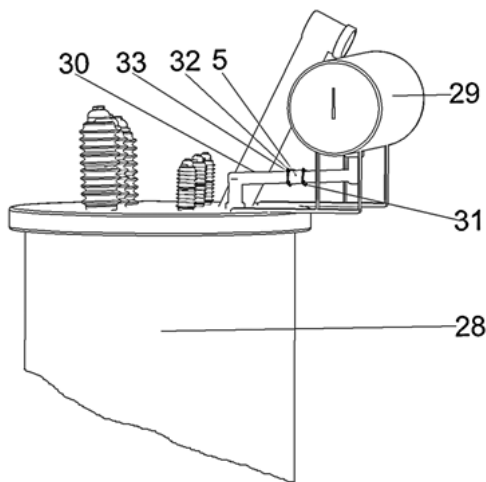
Крепление конструкции газовой защиты трансформатора
